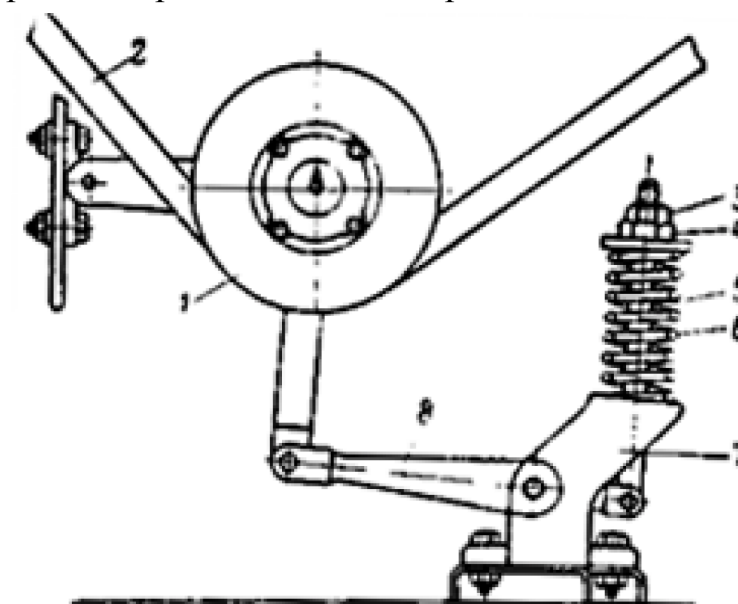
Натяжной механизм привода вентилятора: 1 — натяжной ролик; 2 — ремень; 3 — контргайка; 4 — гайка; 5 — стержень; 6 — пружина; 7 — кронштейн; 8 — рычаг
